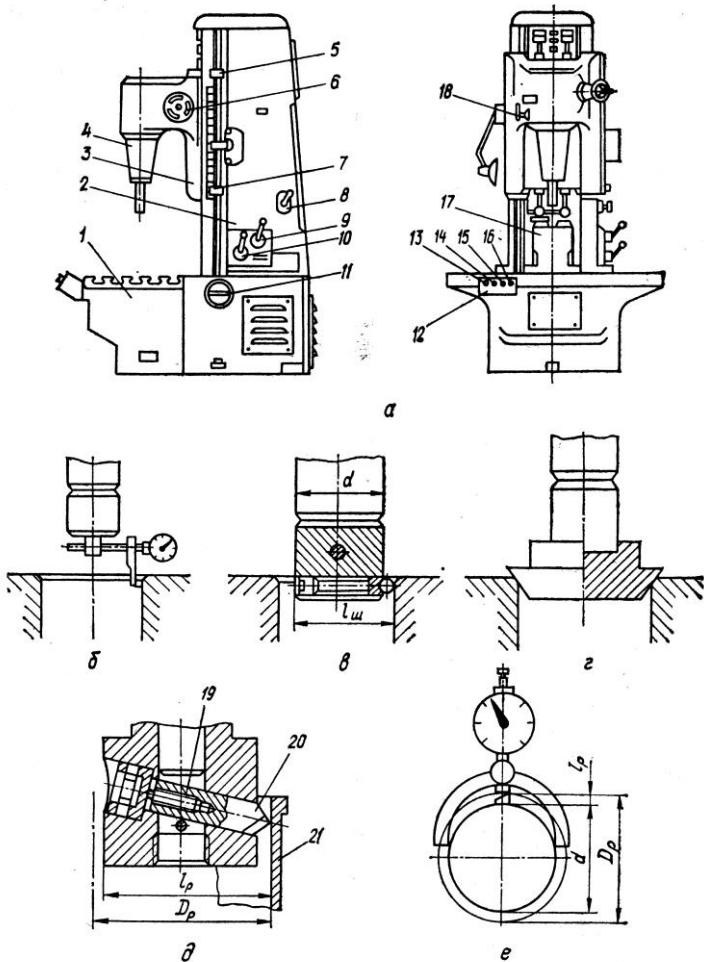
Розточування гільз циліндрів: а – загальний вигляд верстата 2А78Н; б, в, г – центрування гільзи індикаторною голівкою, кулькою, конусом; д – виставлення різця; е – контроль вильоту різця наїзником; 1 – основа; 2 – колона; 3 – шпindelна бабка; 4 – шпindel; 5, 7 – кулачки вимкнення ходу шпindelної бабки; 6 – привод; 8 – перемикач швидкості; 9 – рукоятка переключення подач; 10 – рукоятка переключення обертів шпинделя; 11 – вхідний вимикач
